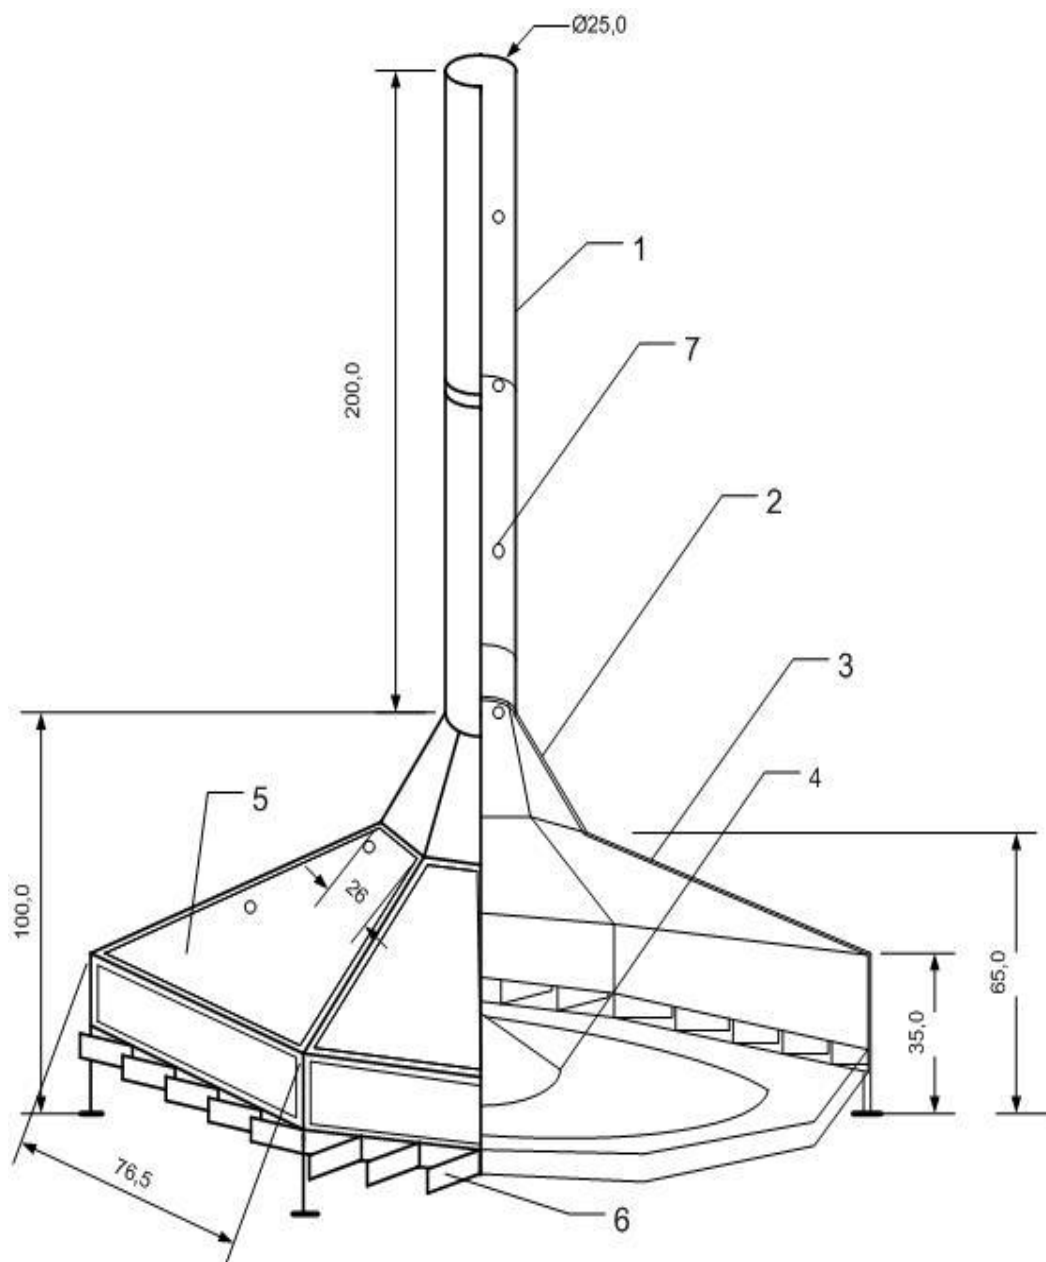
Эскиз общего вида установки. 1 – выводная труба; 2– сглаживающий конус; 3 – парник; 4 – нагреватель-имитатор солнечного облучения; 5 – прозрачная панель корпуса парника – приемник солнечного облучения; 6– направляющие шторки; 7 – точки установки температурных датчиков.
